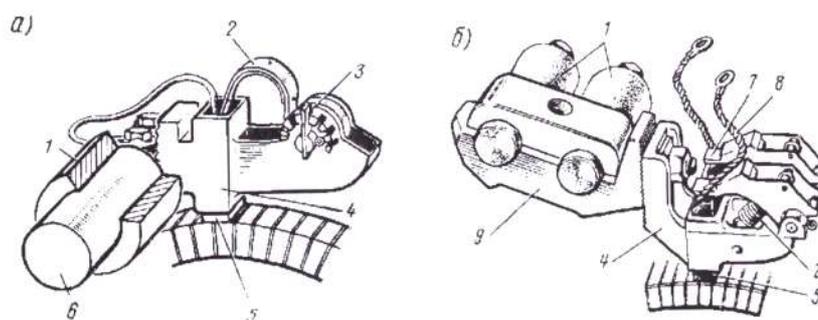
Щеткодержатели вспомогательных машин (а) и тяговых двигателей (б): 1 — изолятор; 2 — пружина; 3 — натяжное устройство; 4 — обойма; 5 — щетка; 6 — щеточный палец; 7 — нажимной малец; 8 — щеточный канатик; 9 — кронштейн
